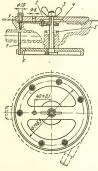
Кондуктор для высверливания сломанных винтов из корпуса насоса стиральной машины «Рига-55»:
